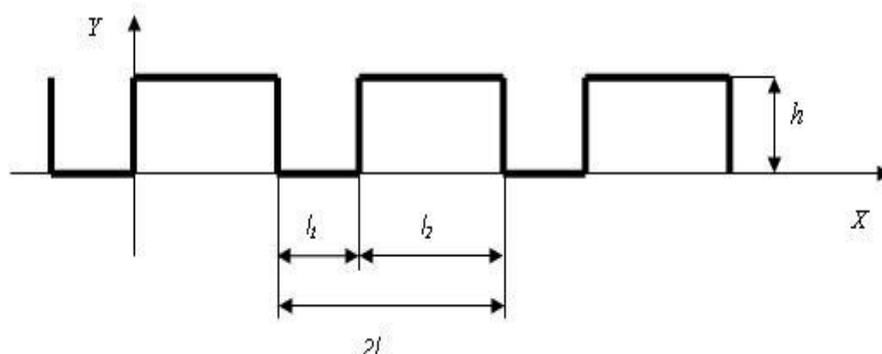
Исходный профиль заготовки прямоугольной формы
